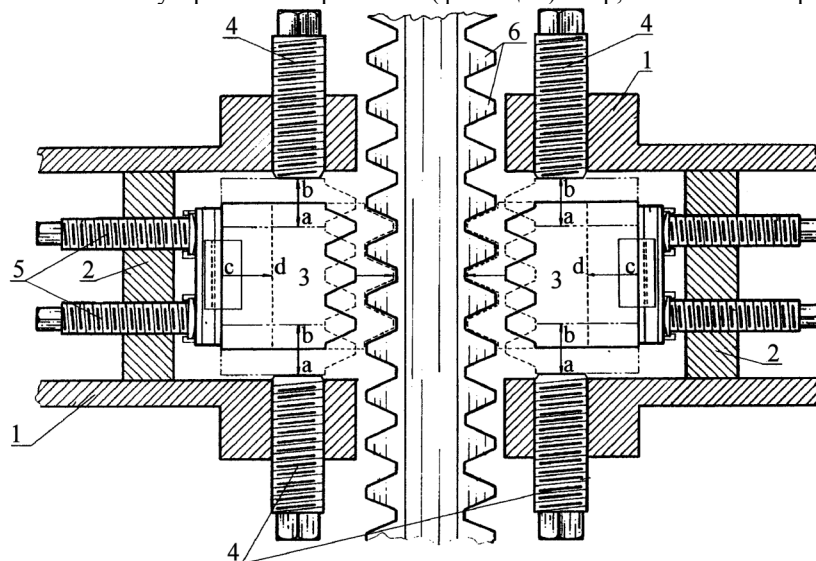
Устройство закрепления (фиксации) опор: 1 и 2 – смежные корпусные конструкции;
